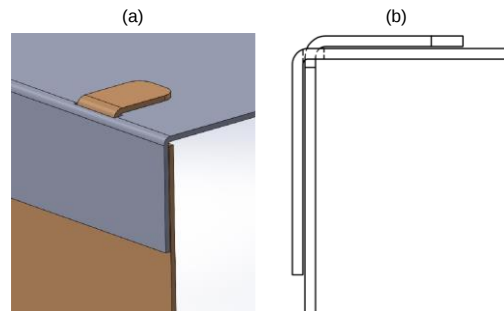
Biegeverlappung dünner Bleche als Beispiel für 4.5.2.9 Verlappen (a) 3-D-Ansicht; (b) technische Zeichnung der Seitenansicht
